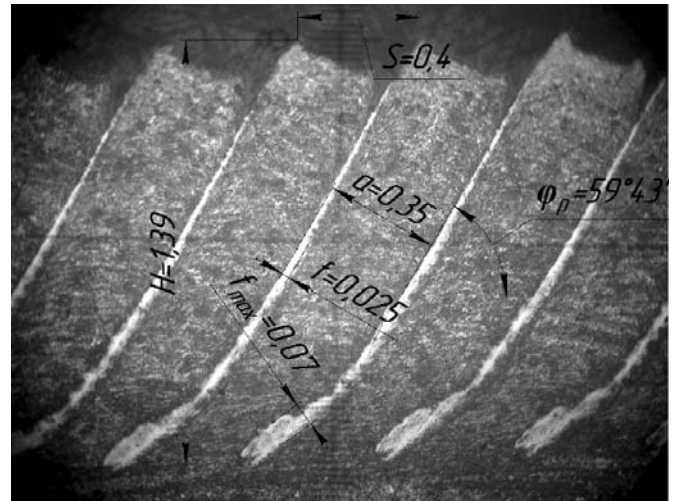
Регулярный макро рельеф на стали 38Х2МЮА
